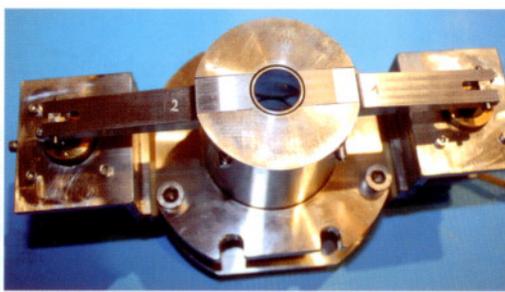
改造后的吹制模塑模具,包括两台步进电机,对直径18mm的柔性环套实现动态变形 / Fig. 10 Retrofitting kit for a blow moulding head containing two stepper drives to dynamically deform the Flex Ring sleeve (diameter 18 mm)
